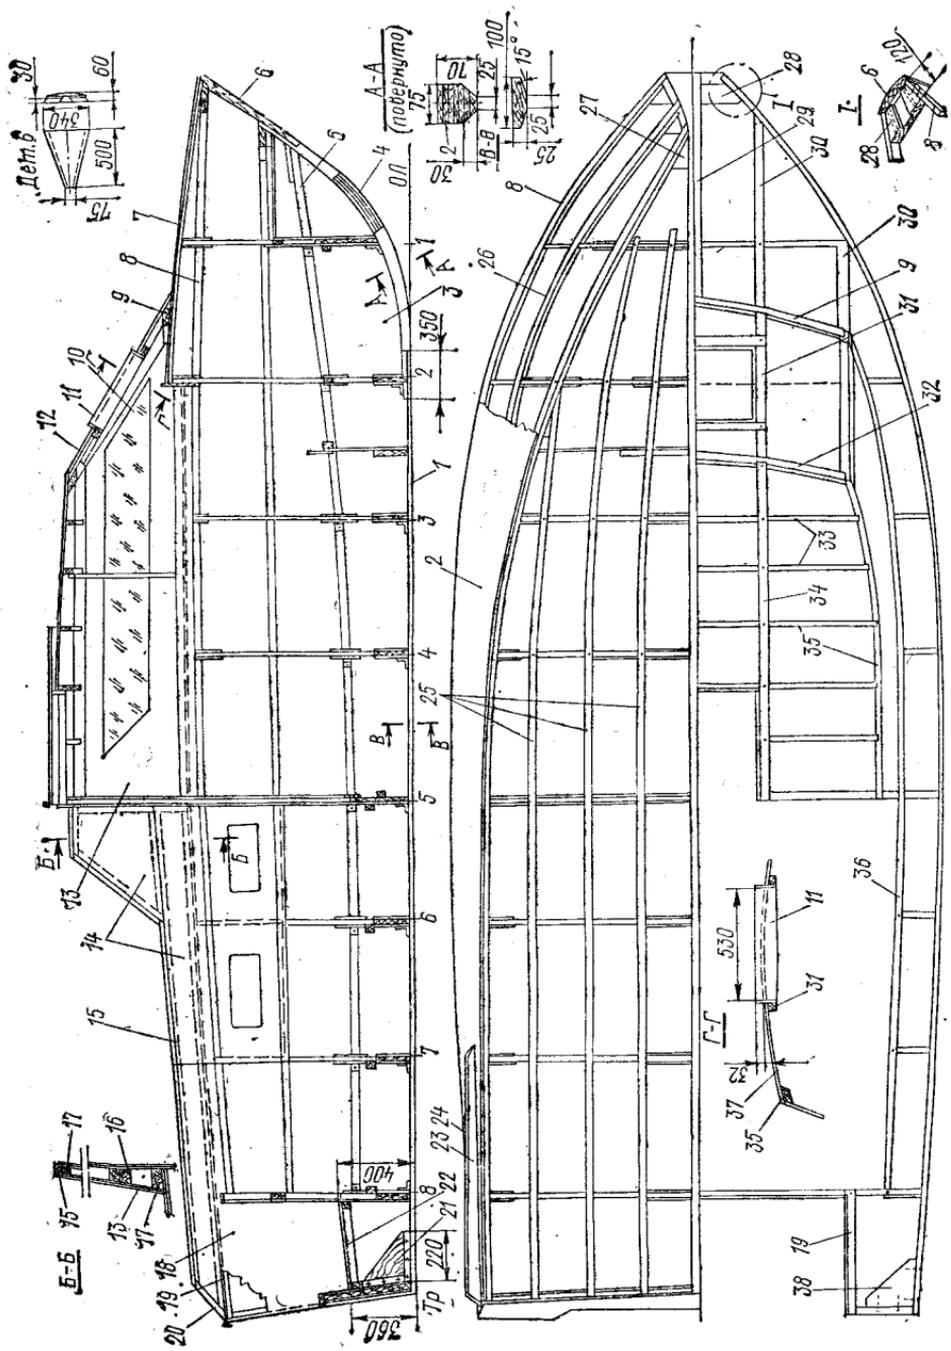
Конструктивный чертеж корпуса (см. рис. 293, а на стр. 328—329).
